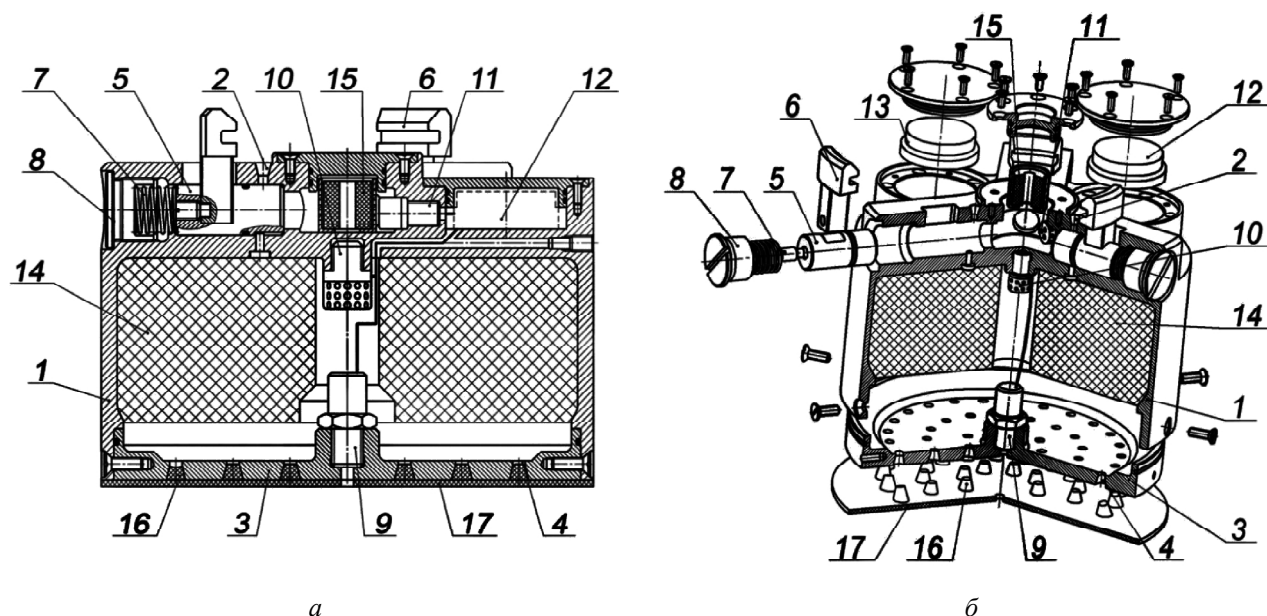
Устройство увеличения дальности полета снаряда: а — устройство в разрезе; б — разнесенный вид устройства. 1 — корпус; 2, 4 — сопловые заглушки; 3 — днище; 5 — поршни; 6 — защёлки; 7 — пружины сжатия; 8 — пробки; 9 — реле давления; 10 — воспламенитель; 11 — воспламенительное устройство; 12 — блок питания и преобразования; 13 — блок управления; 14 — заряд твердого топлива; 15 — заряд пиротехнического состава; 16 — сопловые заглушки; 17 — прокладка
